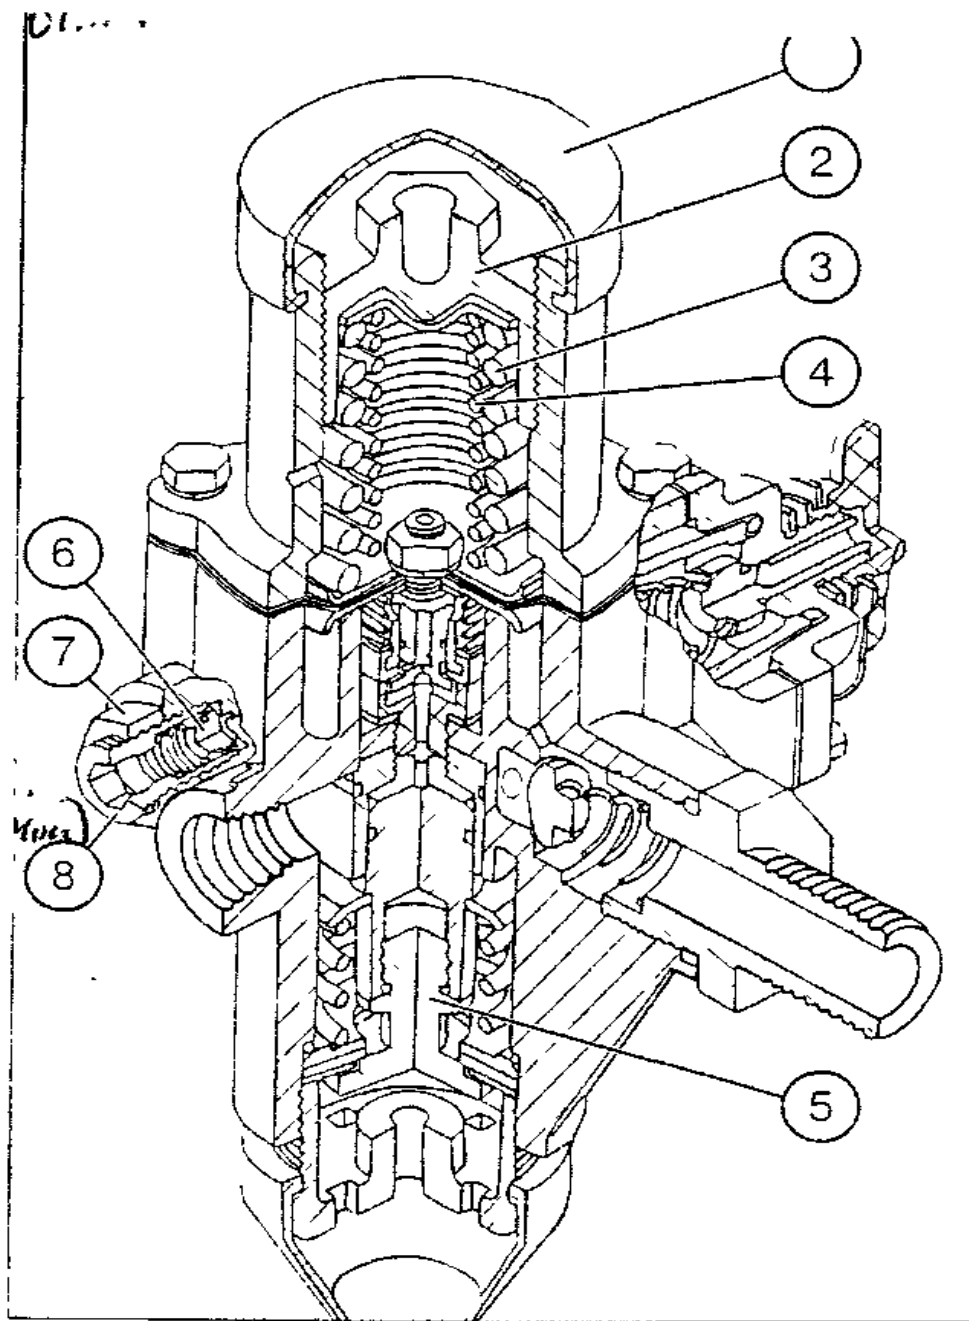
Регулятор давления трактора Беларус 1522: 1 – колпак; 2 – крышка; 3 – пружина наружная; 4 – пружина внутренняя; 5 – клапан разгрузочный; 6 – клапан предохранительный; 7 - контргайка; 8 – винт регулировочный.
